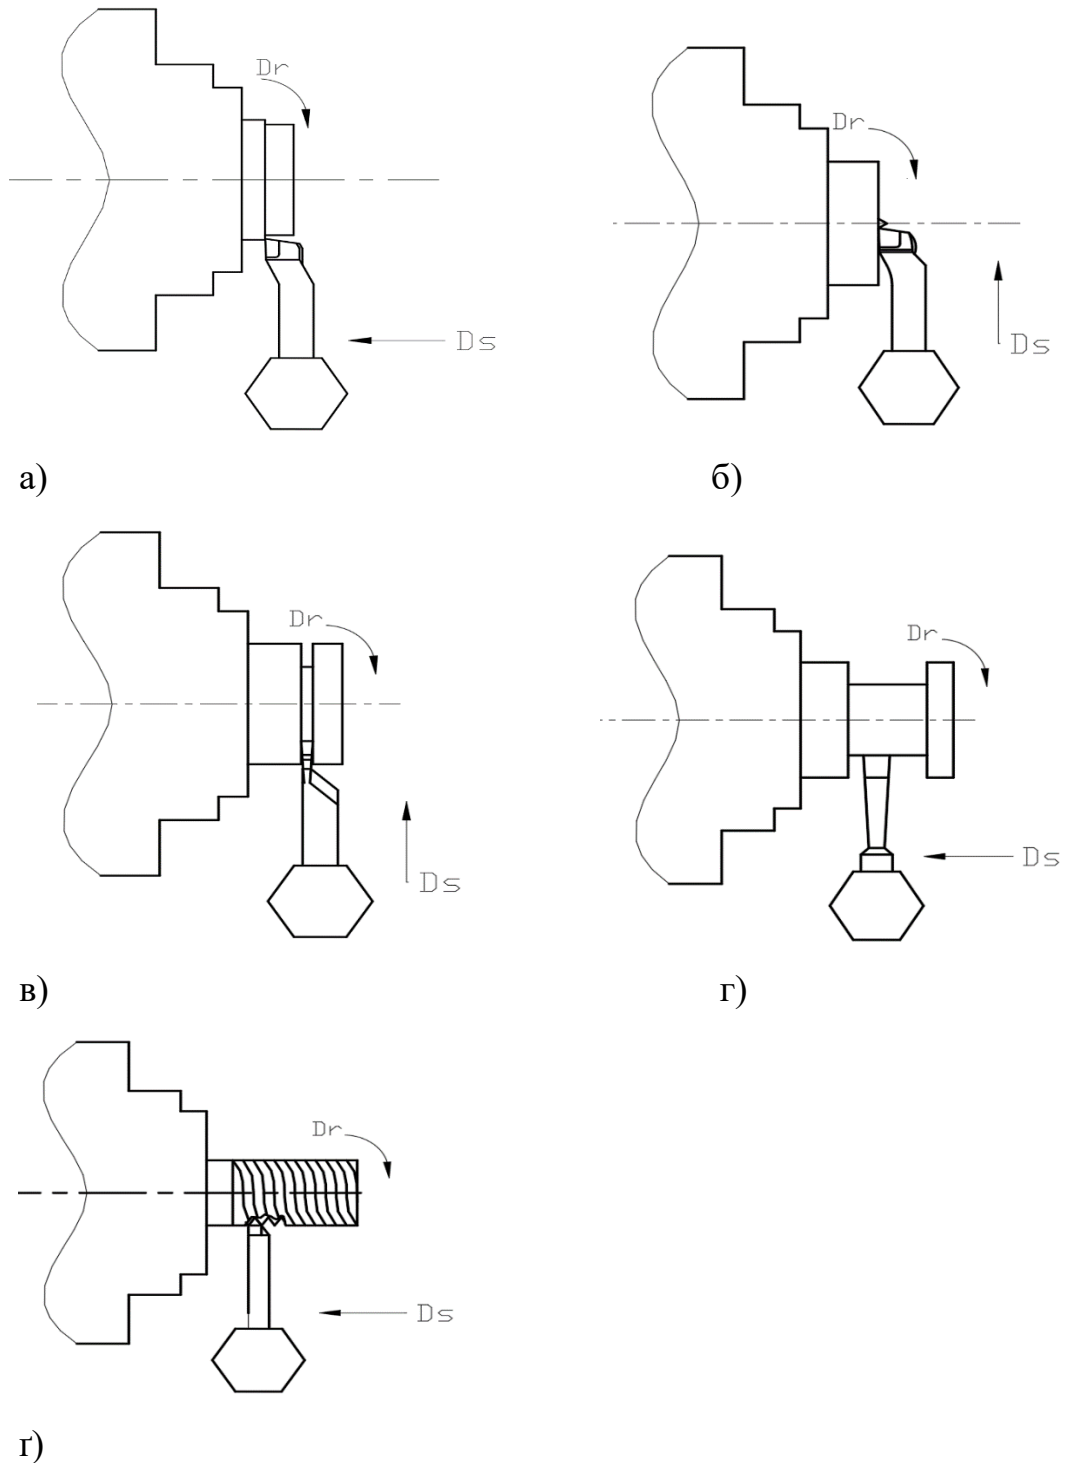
Схеми оброблення поверхонь деталей на токарно-револьверному верстаті [3]: а) поздовжнє точіння; б) підрізка торця; в) відрізання; г) прорізання паза; г) нарізання різі різцем .
